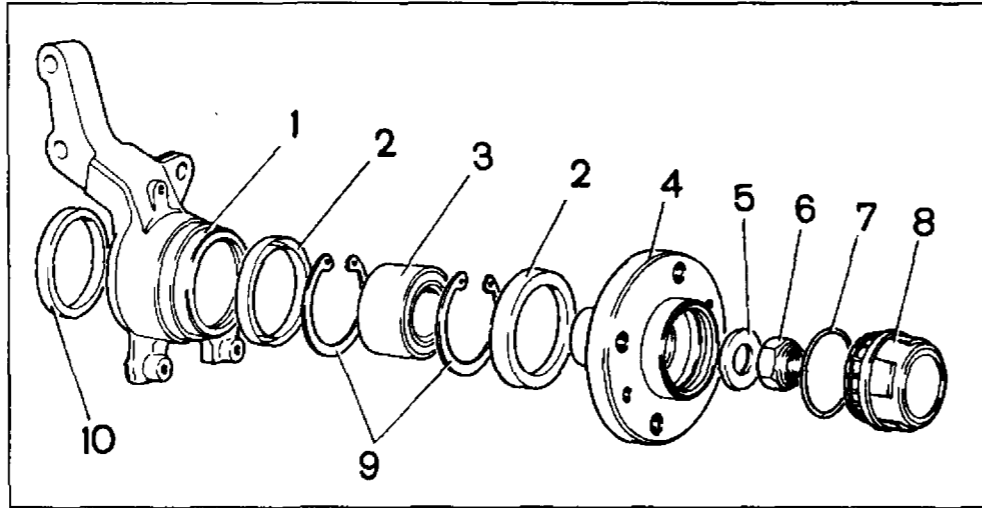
Поворотный кулак и детали ступицы переднего колеса:
